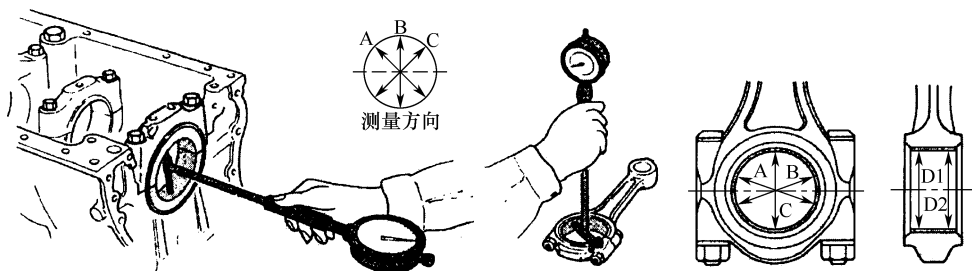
曲轴轴承座孔和连杆轴承座孔的直径测量方法
